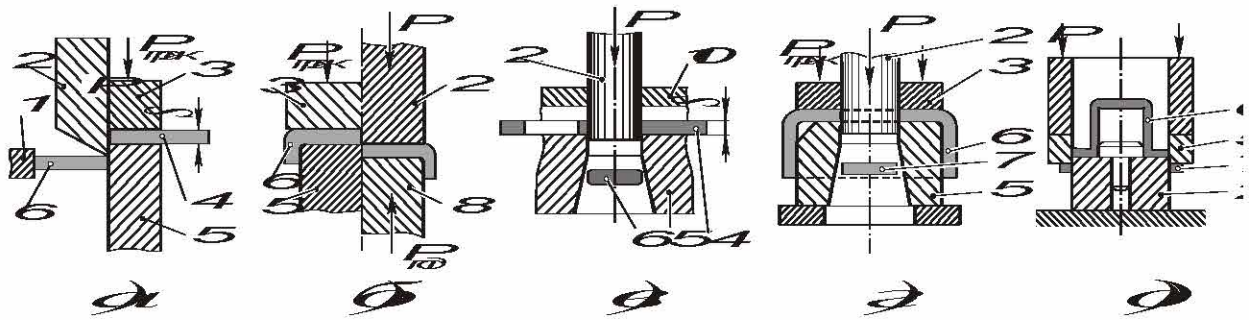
Схеми основних розділових операцій листового штампування: а – відрізання; б – розрізання; в – вирубка; г – пробивання; д – обрізання; 1 – упор; 2 – пуансон; 3 – притискач; 4 – вихідна заготовка; 5 – матриця; 6 – заготовка; 7 – відхід; 8 – виштовхувач; 9 – підкладна плита; 10 – знімач.
